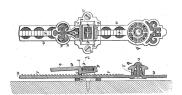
Máquina de corte Pearson. Fuente: Google Patents.
